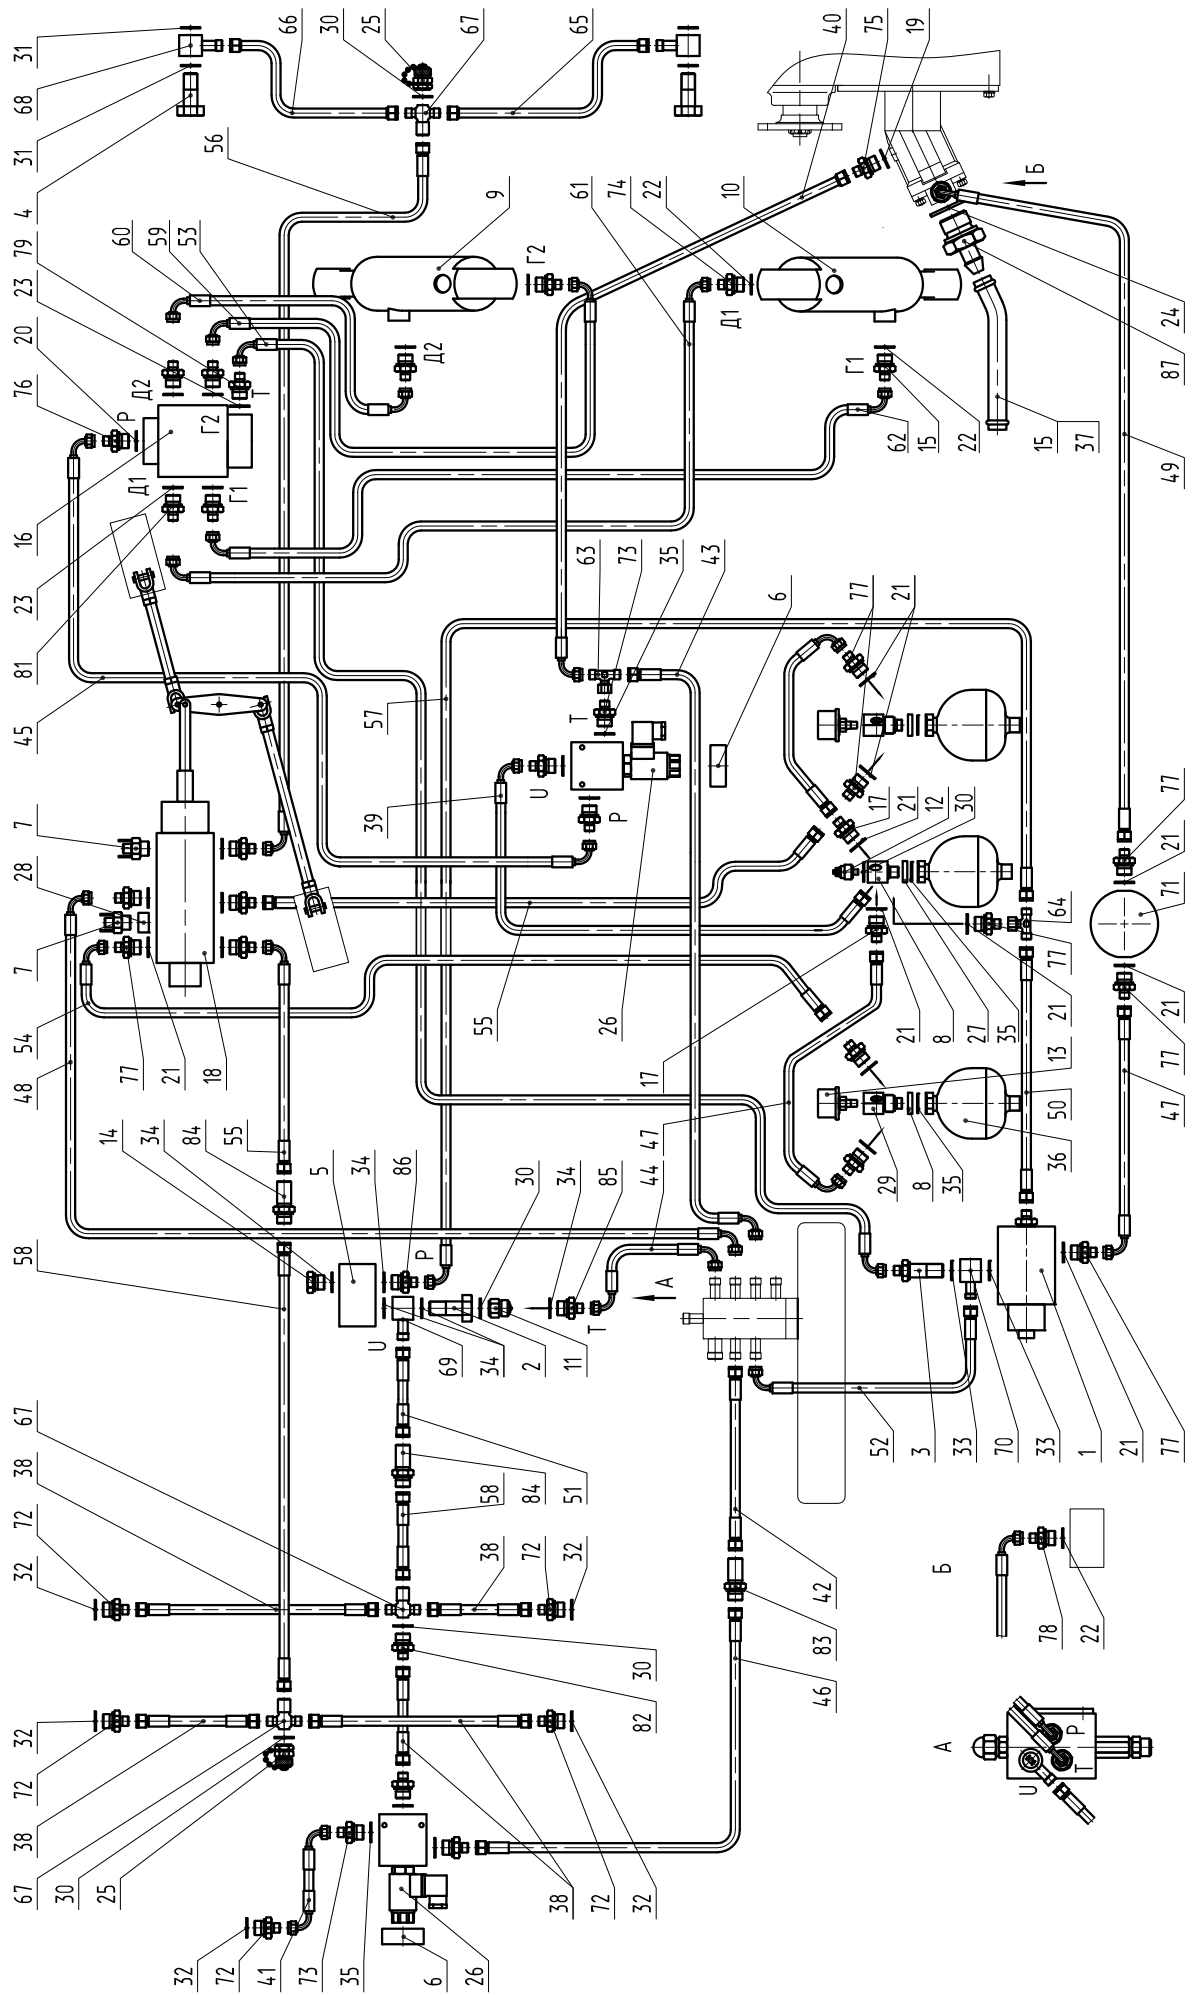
Монтажная схема привода тормозов с гидроцилиндрами для блокировки качания подмоторного моста
